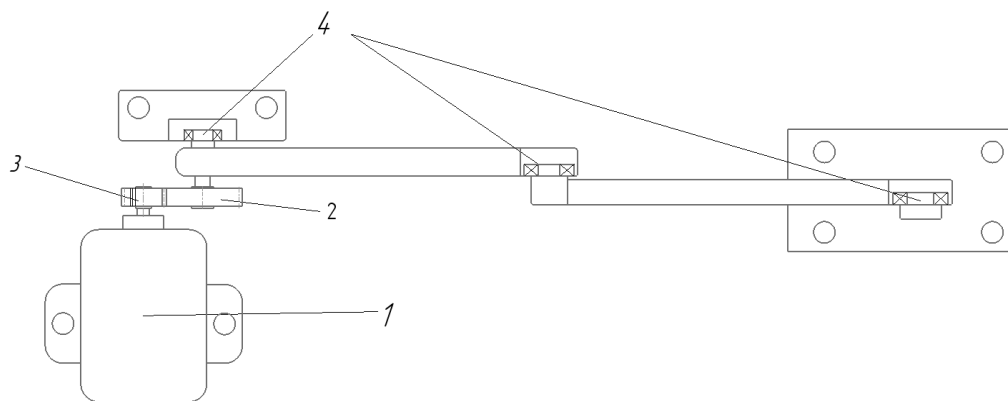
Схема устройства для преобразование механической энергии в электрическую (1-генератор, 2-зубчатое колесо, 3- шестерня, 4-подшипник)
